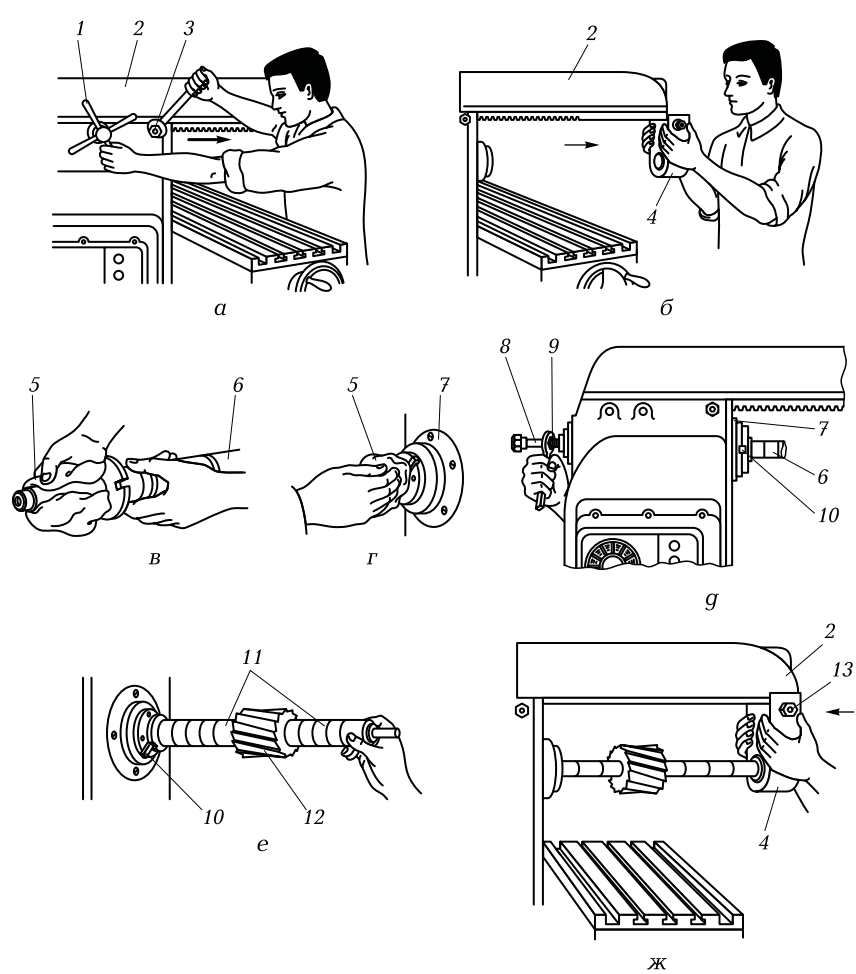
Последовательность установки и закрепления цилиндрической фрезы на горизонтально-фрезерном станке:
